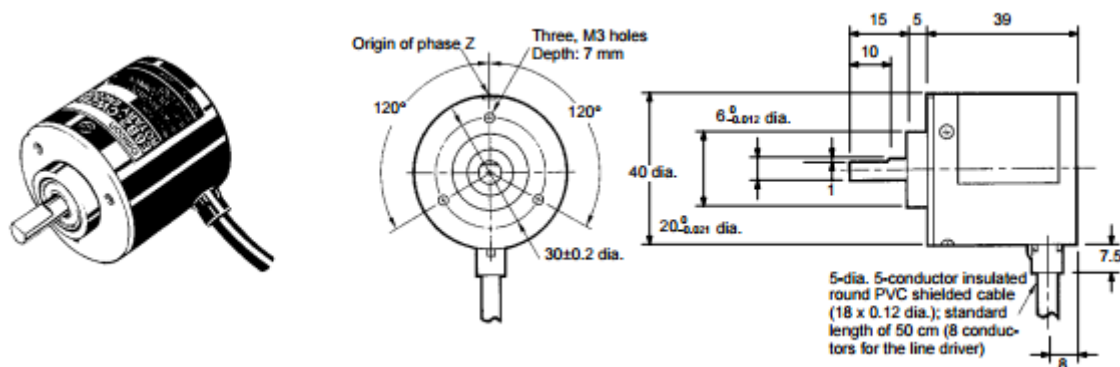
Внешний вид и габаритные размеры энкодера E6B2-CWZ6C.
